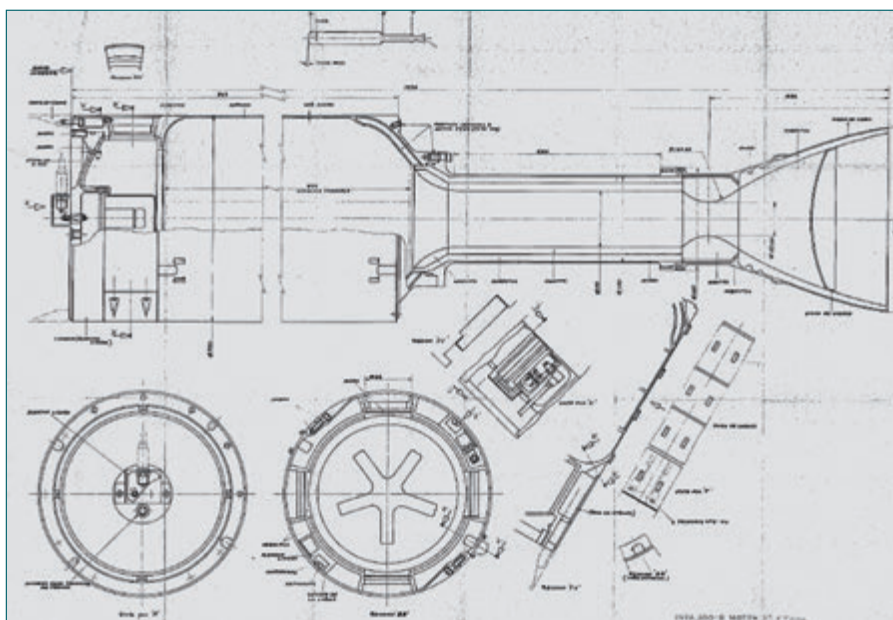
Plano del motor de 3ª etapa del INTA-300G. ■
